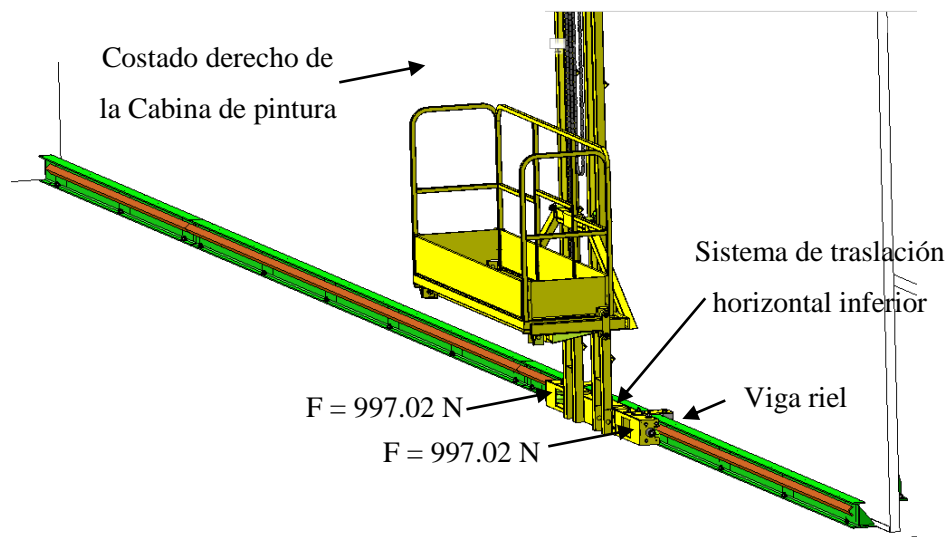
Aplicación de la fuerza F en la viga riel para el sistema de traslación horizontal inferior
